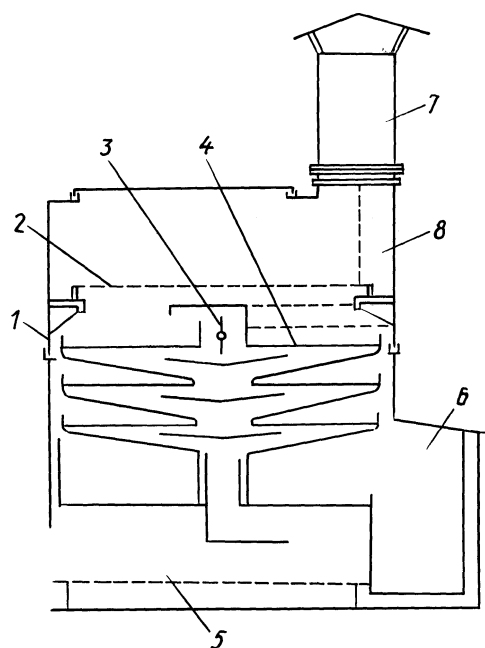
Устройство для непрерывного плавления, обезвоживания, разогрева и очистки битума:
